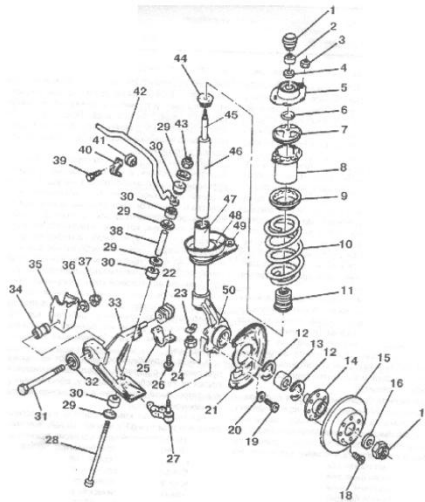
Елементи конструкції підвіски переднього колеса автомобілів Seat: 1 - захисний ковпачок; 2, 3, 24, 37, 43 - гайки; 4, 20, 29, 32, 36 - шайби; 5 - верхня опора амортизаторної стійки; 6 - упорна шайба; 7 - пластмасова опора; 8 - захисна склянка; 9 - верхня опорна чашка; 10 - пружина підвіски; 11 - буфер ходу стиску; 12 - стопорне кільце; 13 - підшипник маточини; 14 - маточина колеса; 15 - гальмівний диск; 16 - стопорна шайба; 17 - фасонна гайка; 18, 19 - гвинт; 21 - захисний кожух; 22 - втулка заднього шарніра важеля підвіски; 23 - чека; 25, 40 - кронштейни; 26, 28, 31, 39 - болти; 27 - кульова опора; 30 - втулка стабілізатора; 33 - важіль підвіски; 34 - втулка переднього шарніра важеля підвіски; 35 - елемент корпусу кузова автомобіля; 38 - розпірна втулка; 41 - подушка стрижня стабілізатора; 42 - стрижень стабілізатора; 44 - гайка корпусу стійки; 45 - шток; 46 - циліндр; 47 - корпус стійки; 48 - нижня опорна чашка; 49 - поворотний важіль; 50 - поворотний кулак
